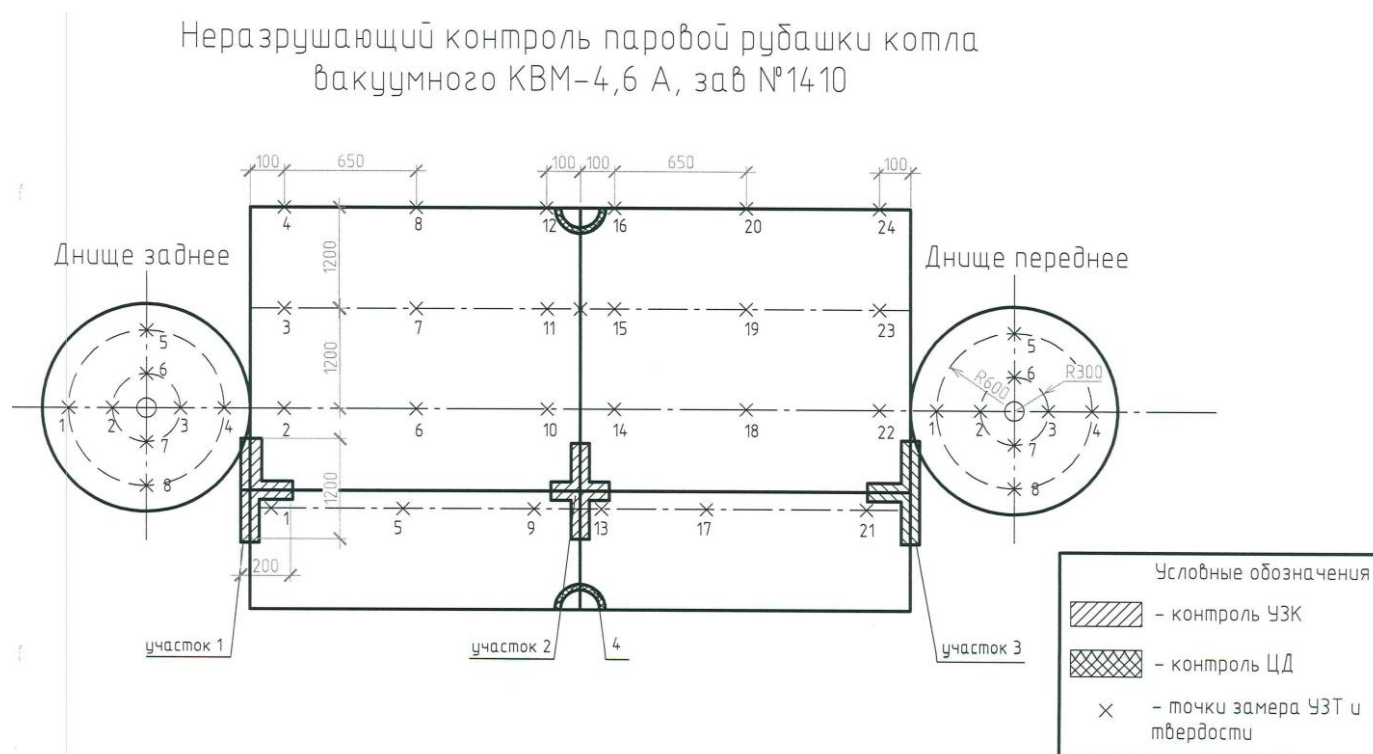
Схема неразрушающего контроля паровой рубашки котла КВМ-4,6А
